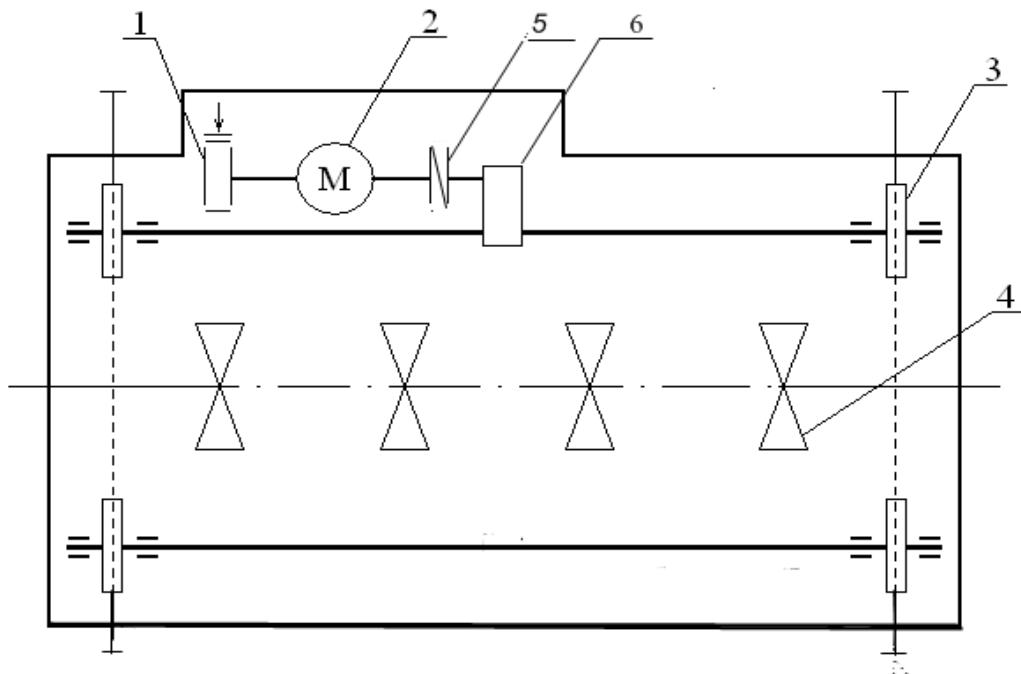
Кинематическая схема передвижного рольганга № 14:
